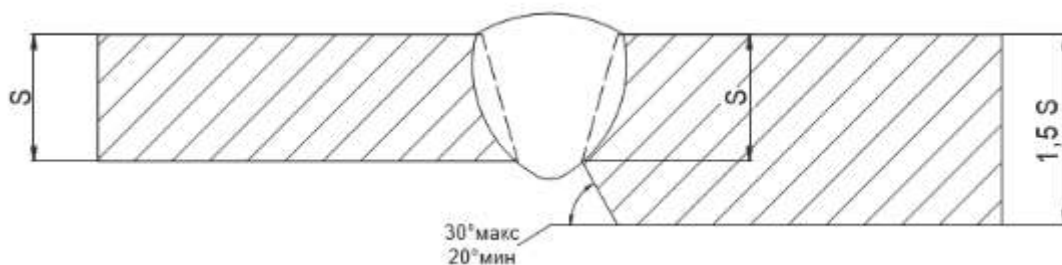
Конструктивные размеры разделки кромок и сварных швов разнотолщинных труб (до 1,5 толщины стенки)
